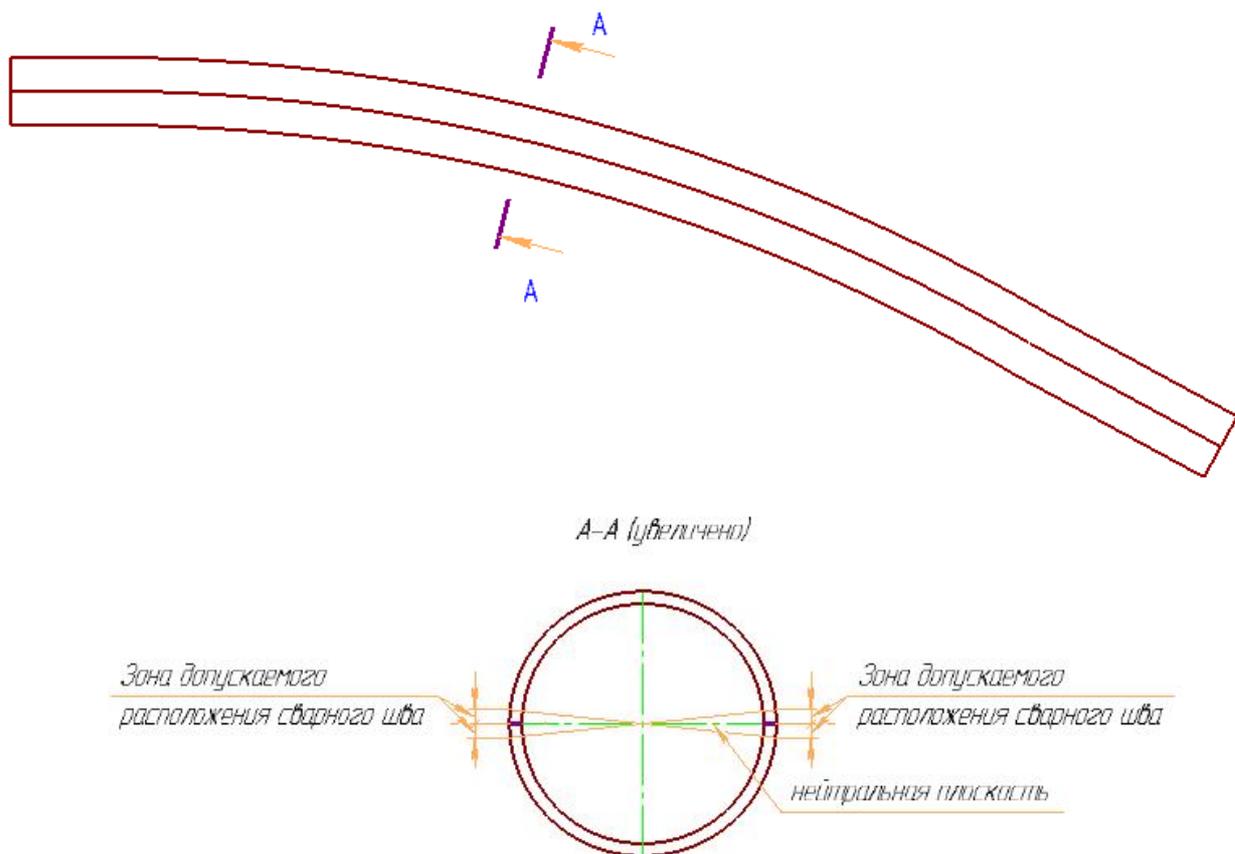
Расположения продольного сварного шва при гибке
